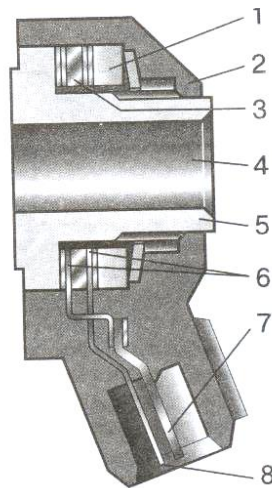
Конструкція датчика детонації фірми BOSCH: 1 – гравітаційна маса; 2 – корпус; 3 – п'єзокерамічне кільце; 4 – отвір для болта кріплення; 5 – металева втулка; 6 – контактні пластини; 7, 8 – контакти рознімання
